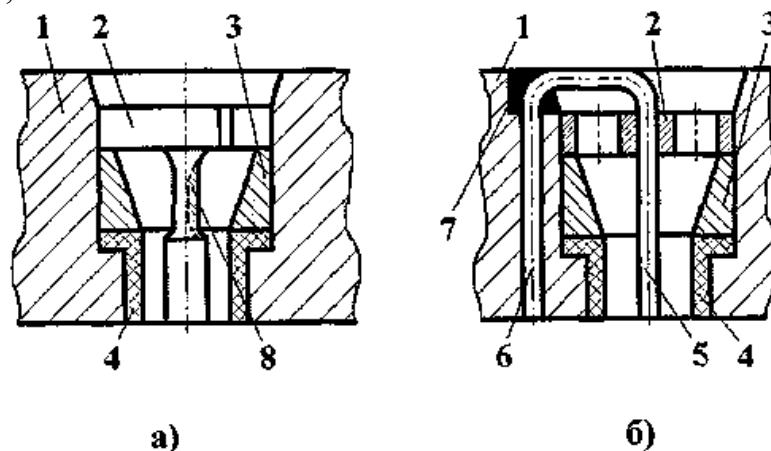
Матриці макаронних пресів для формування трубчастих виробів: а – коротких; б – довгих; 1 – корпус; 2 – вкладиш; 3 – проміжне кільце; 4 – вставка з фторопласту або тефлону; 5 – трубка; 6 – отвір у корпусі матриці; 7 – місце пайки; 8 – виріз у вкладиші для формування зігнутих макаронних виробів
